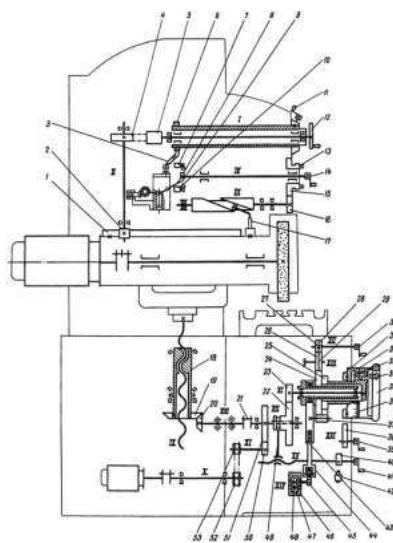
Кинематическая схема плоскошлифовального станка 3Б722
